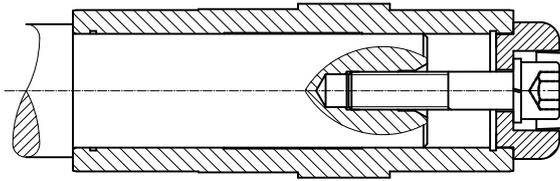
riduttore fissato ad un albero con spallamento mediante elemento di fissaggio
